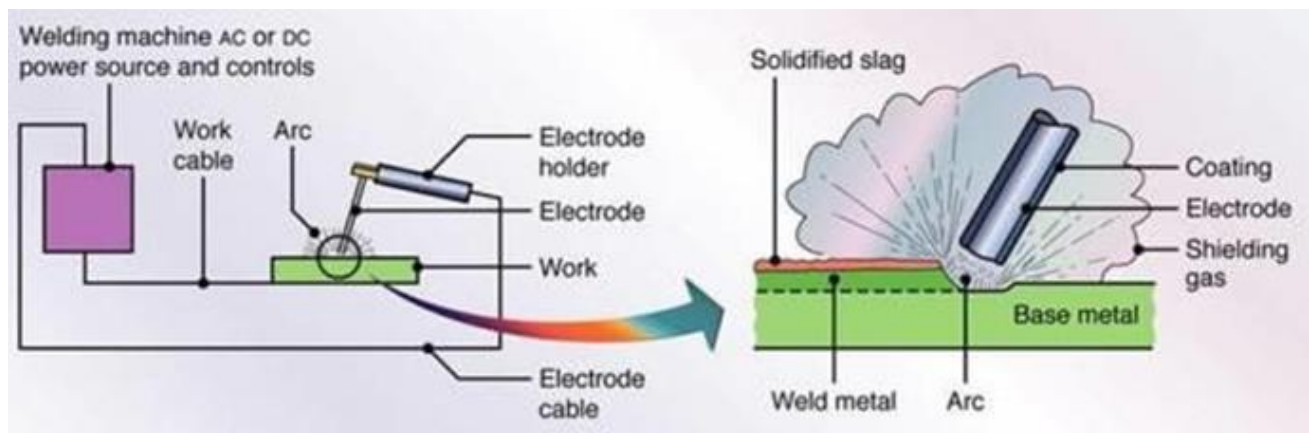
Схема ручного дугового зварювання покритими електродами [5]
